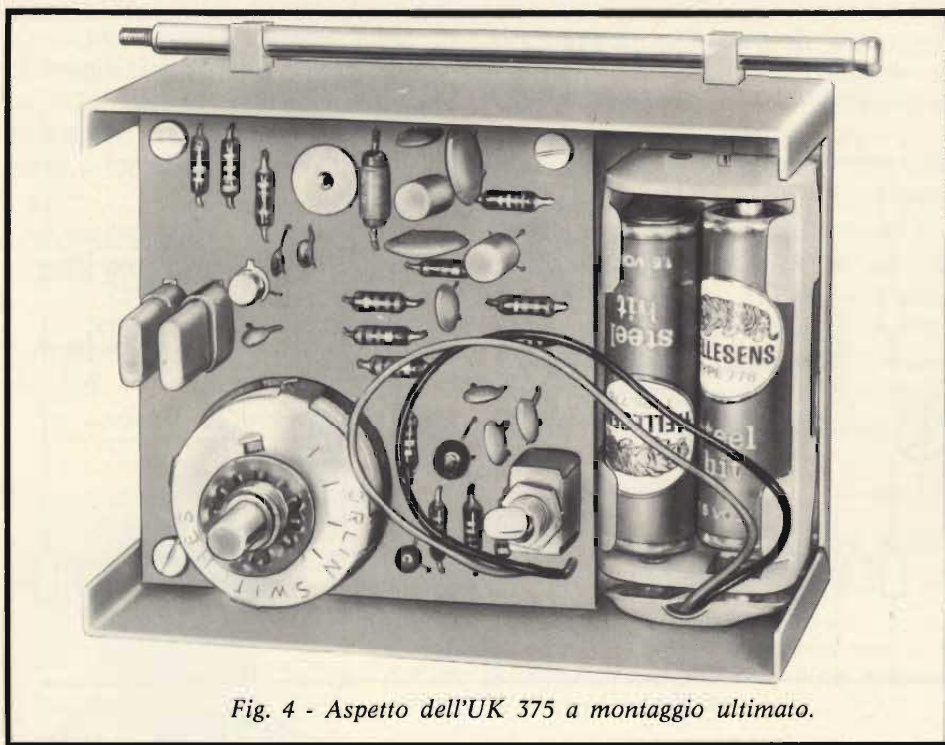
Aspetto dell'UK 375 a montaggio ultimato.
